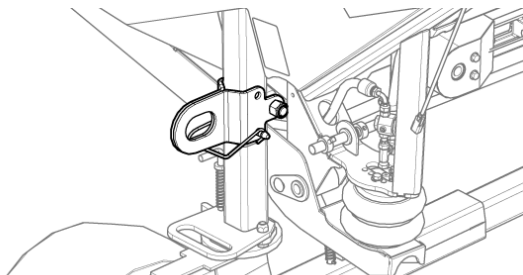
Проверка прижимного устройства оси сцепного стержня.
